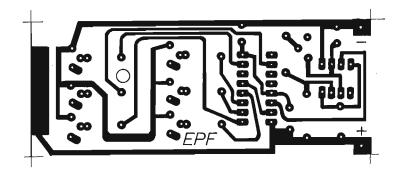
Disegno in grandezza reale del circuito stampato da riprodurre su una basetta di materiale isolante, di forma rettangolare, delle dimensioni di 9 cm x 3,5 cm.
